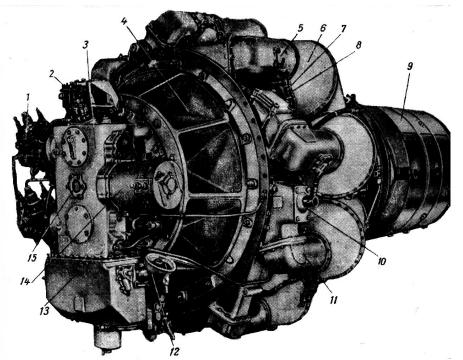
,а. Общий вид ТРД с центробежным компрессором.
